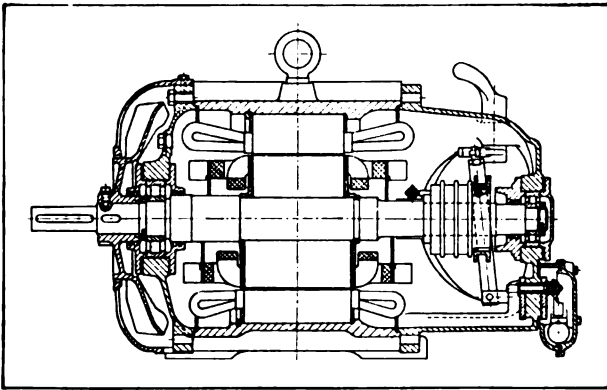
Motor mit Mantelkühlung (Längsschnitt).
